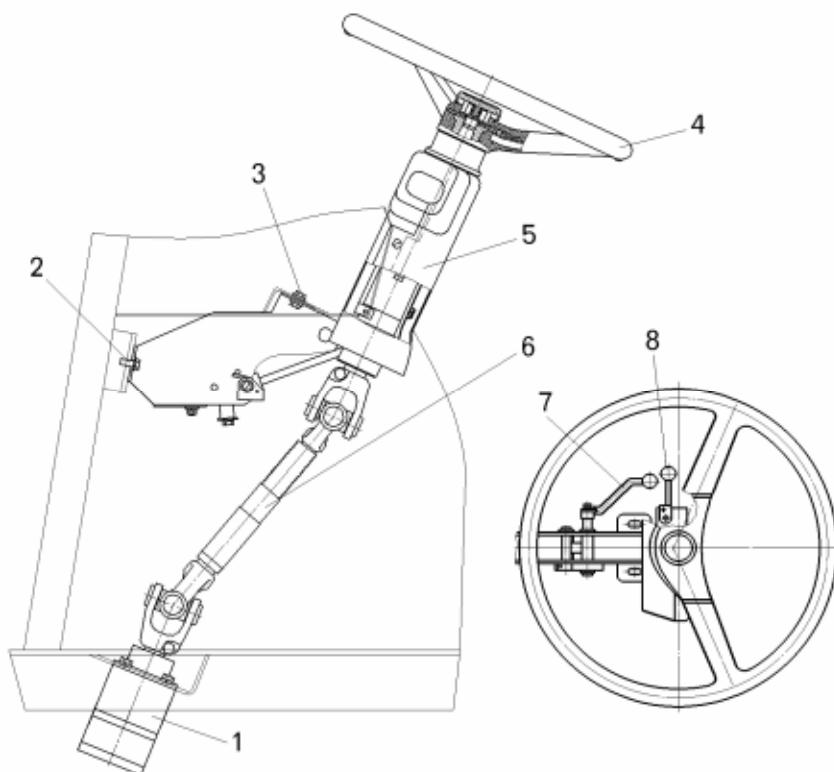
Механический привод гидравлического рулевого механизма:
